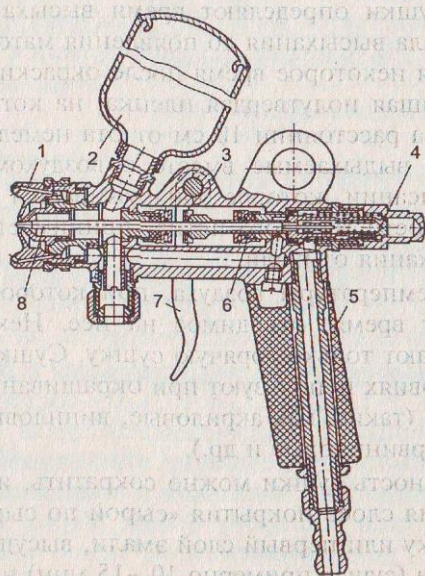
Пневматический пневмораспылитель: 1 — распылительная головка; 2 — бачок для краски; 3 — корпус распылителя; 4 — запорный винт; 5 — ручка; 6 — прокладка; 7 — спусковой крючок; 8 — запорная игла
